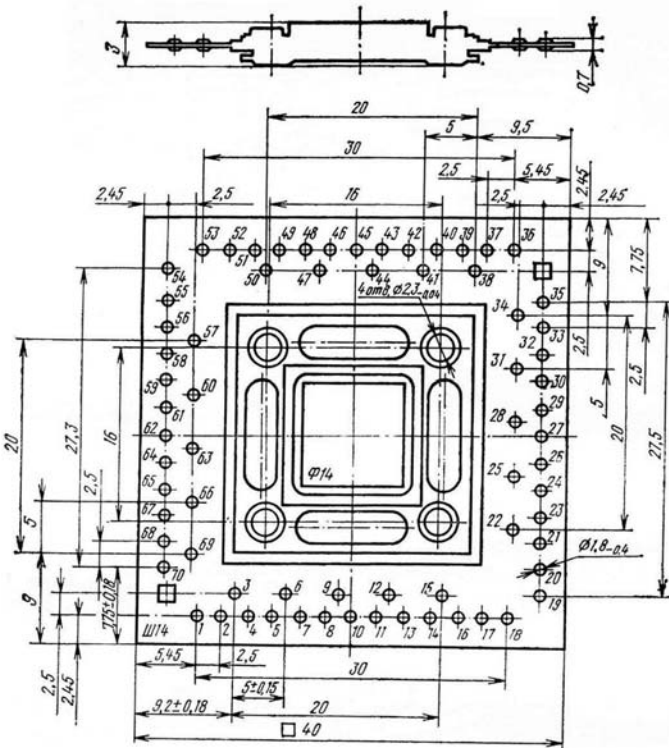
Внешний вид и габаритные размеры ФПУ-14А (Б)
